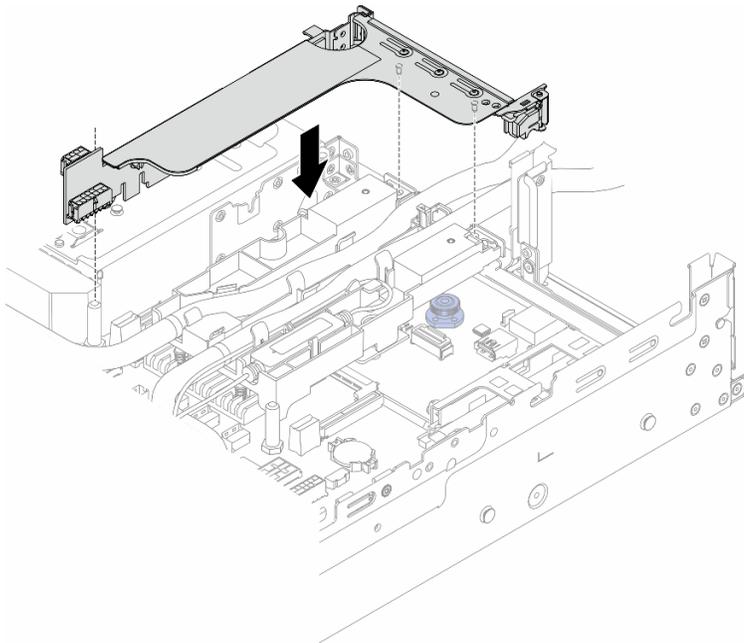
Installation du boîtier de la carte mezzanine 1FH
